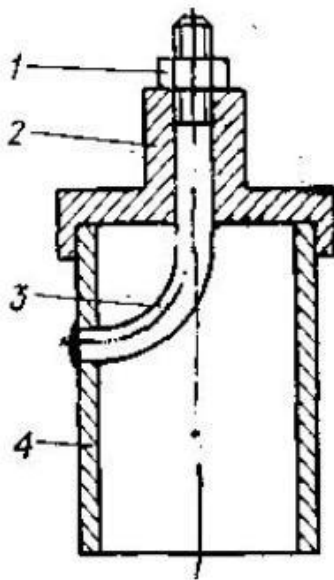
Приварка шпильки до корпусу ковпачка:
